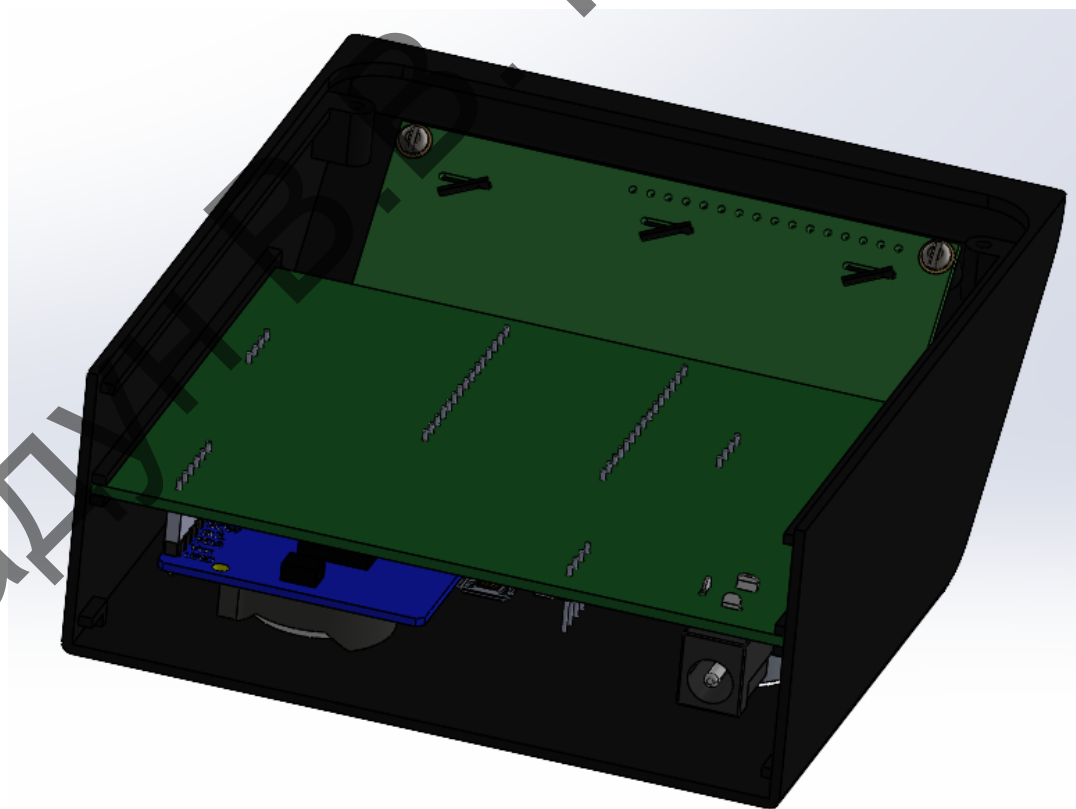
Встановлення дисплею та друкованого вузла в корпусі.
